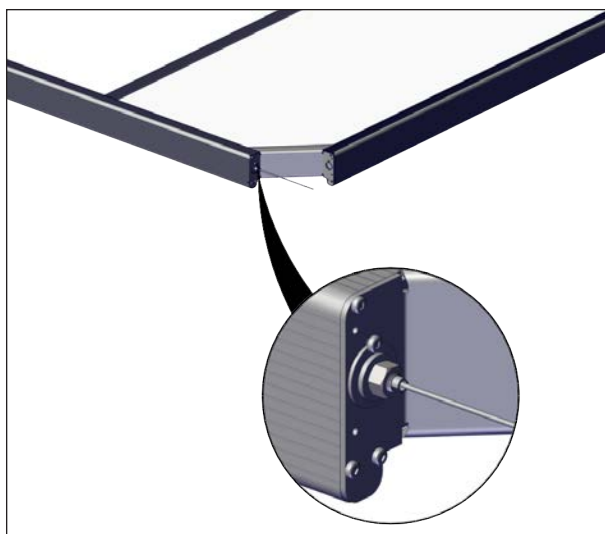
INSERTION DE L'ASSEMBLAGE DU GRIPLOCK DANS LA DOUILLE DE GUIDAGE HEXAGONALE
